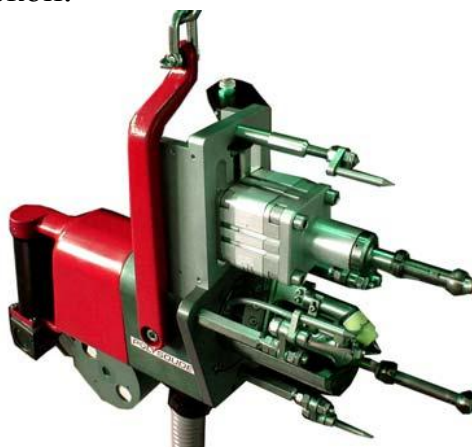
Сварочная головка фирмы «Polysoude» TS-2000.
